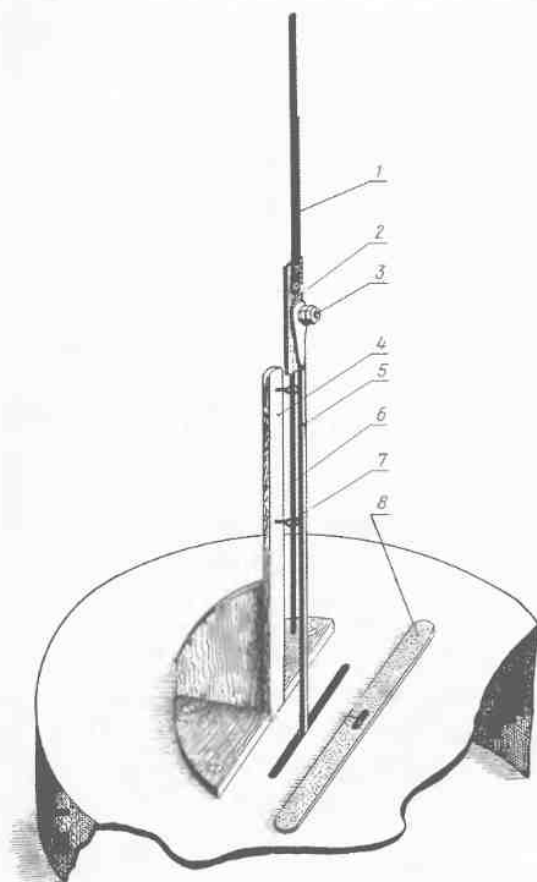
Соединение шатуна с державкой ползуна и с пилкой (вид на часть крышки): 1 — пилка; 2 — державка пилки и шатуна; 3 — ось колебания шатуна; 4 — стойка; 5 — шатун; 6 — стержень ползуна; 7 — направляющие кольца ползуна; 8 — войлочная накладка на щель крышки кожуха
